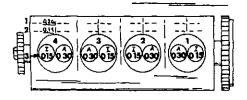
Схема регулировки зазоров клапанов. Строка 1 = Измеренный зазор клапана Строка 2 = Разность между зазором клапана и собственно зазором
